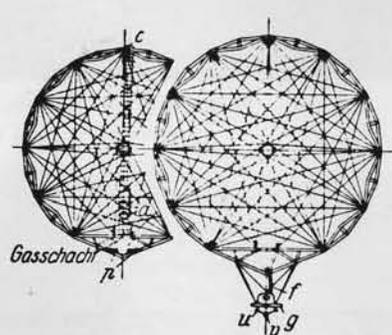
Querschnitt am Haupttring der hinteren Maschinengondel
